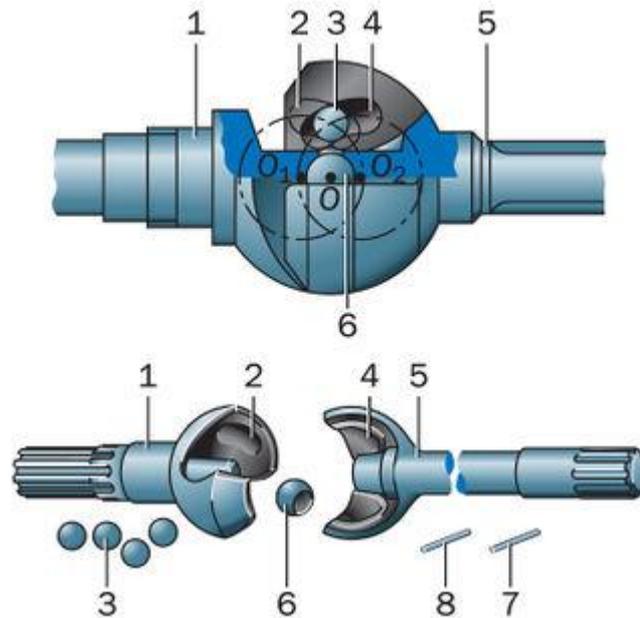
Шарнир с делительными канавками типа «Вейс»:
